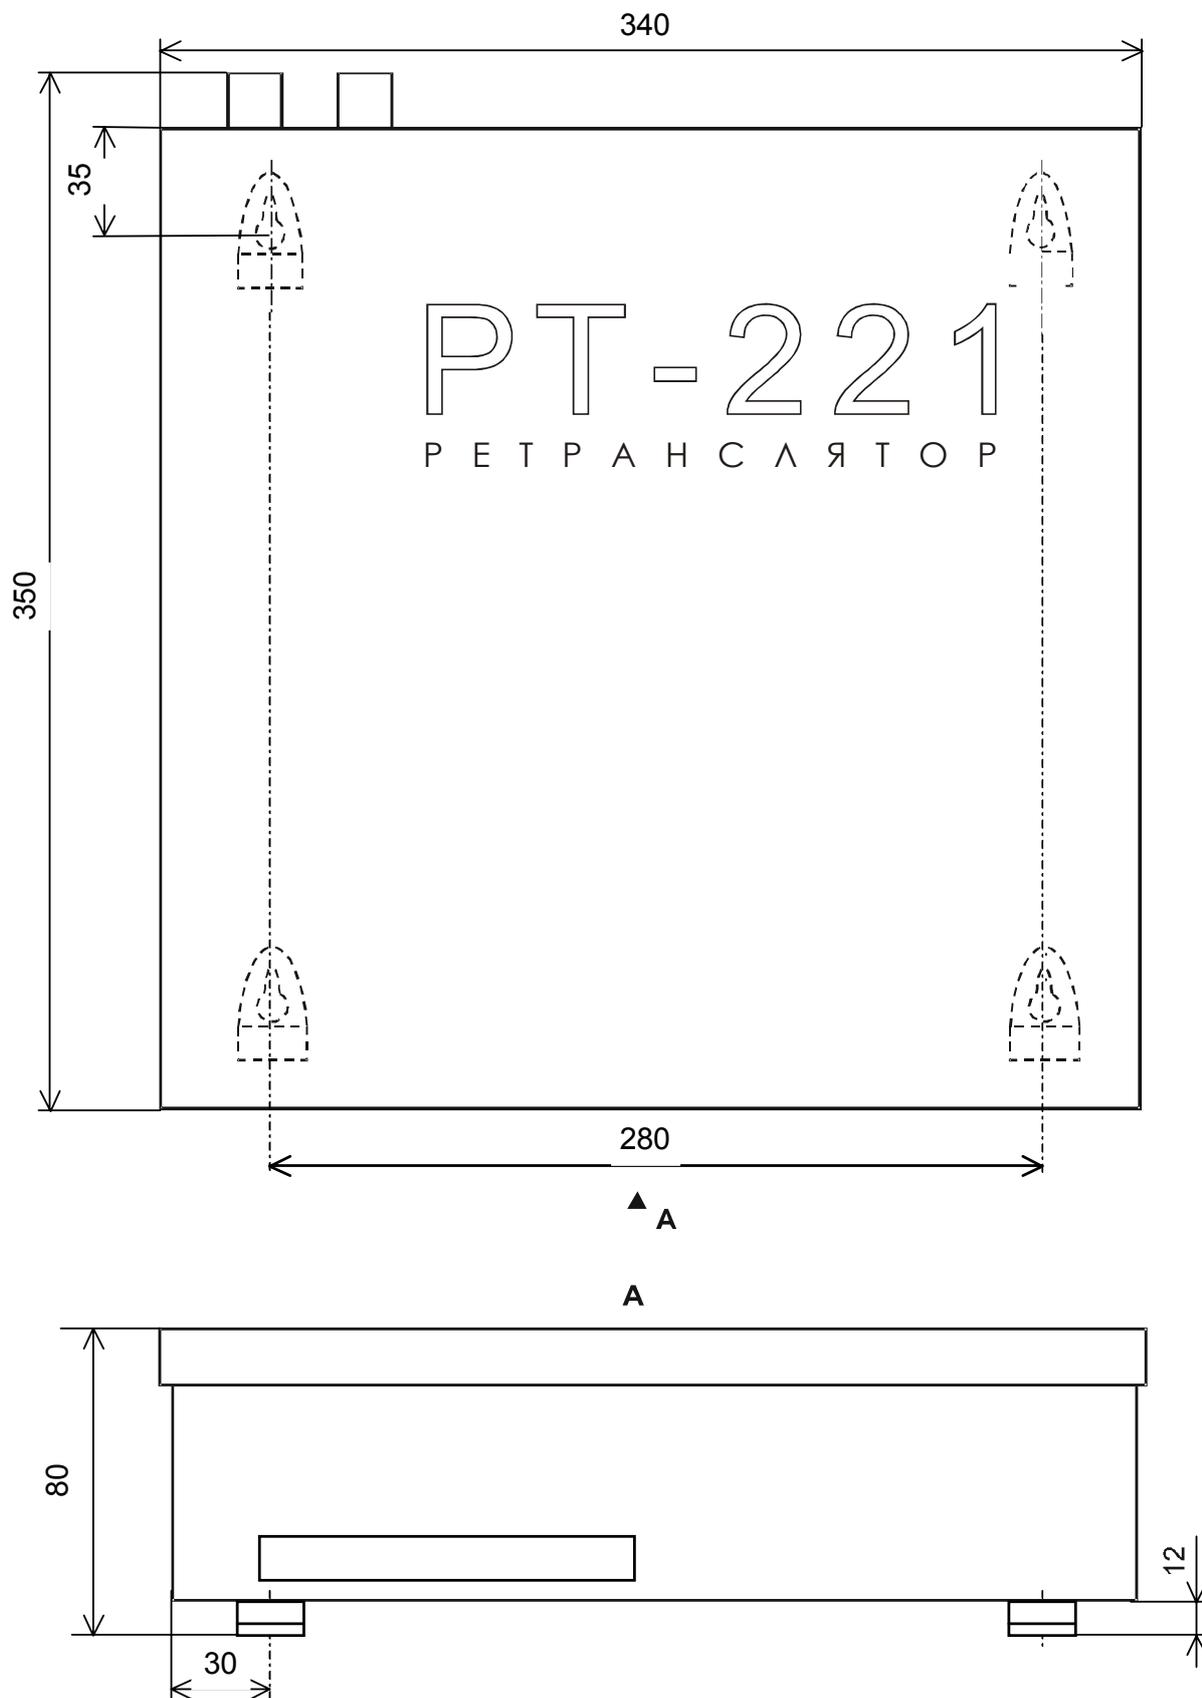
Габаритные и установочные размеры ретранслятора
